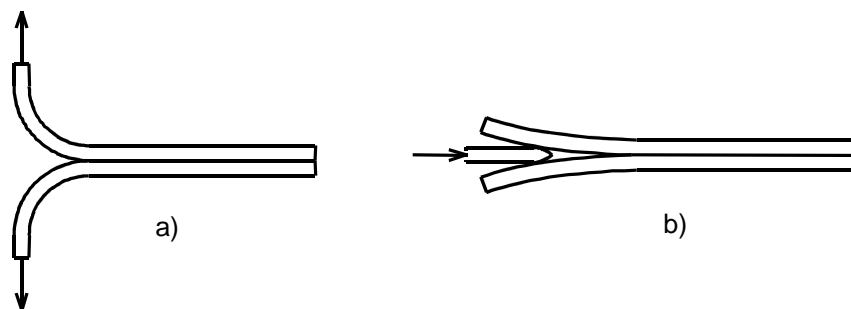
Ensaios de clivagem de juntas coladas: a) ASTM D1876; b) ASTM D3762
